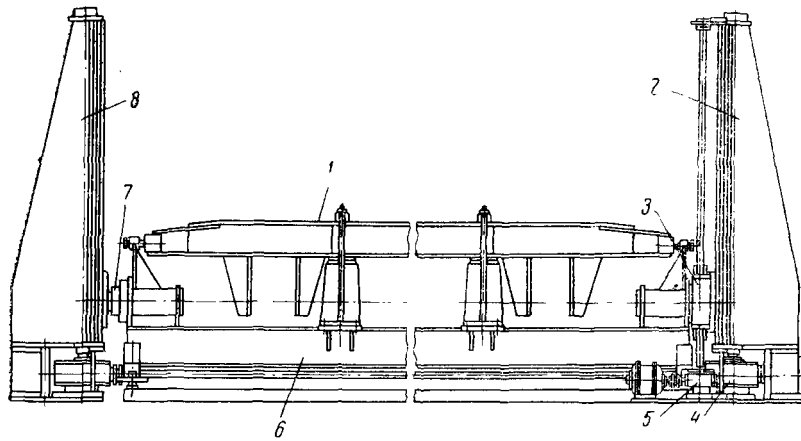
Подъемно-поворотный кантователь для сварки рам:
